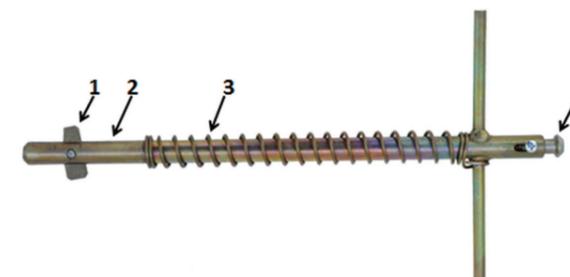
Ключ крышки люка ККЛ-0: 1 – пластина; 2 – корпус; 3 – пружина; 4 – толкатель. Ключ приобретается при закупке партии устройств УЗЛ-Л ССД.
